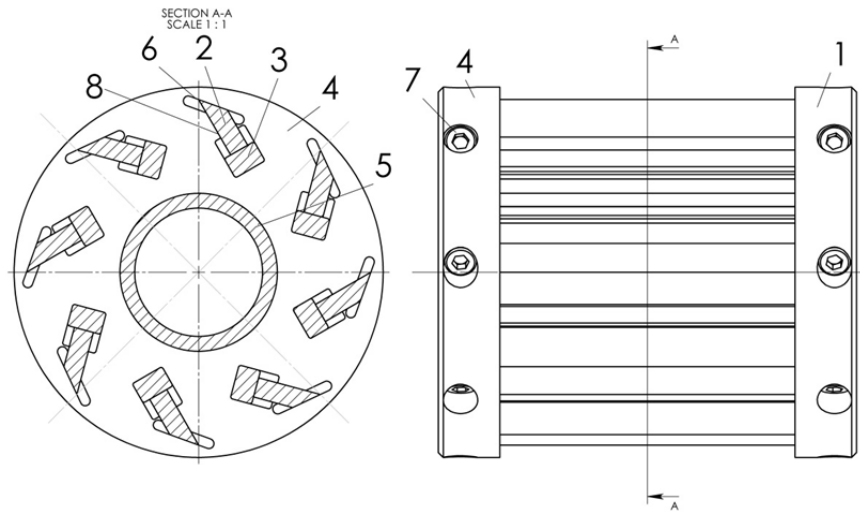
Фреза циліндрична збірна безкорпусна з самовстановними ножами: 1, 4 – фланці; 2 – ніж; 3 – підтискаюча планка; 5 – втулка; 6 – базувальна поверхня паза; 7 – гвинт; 8 – прорізь для ножа
